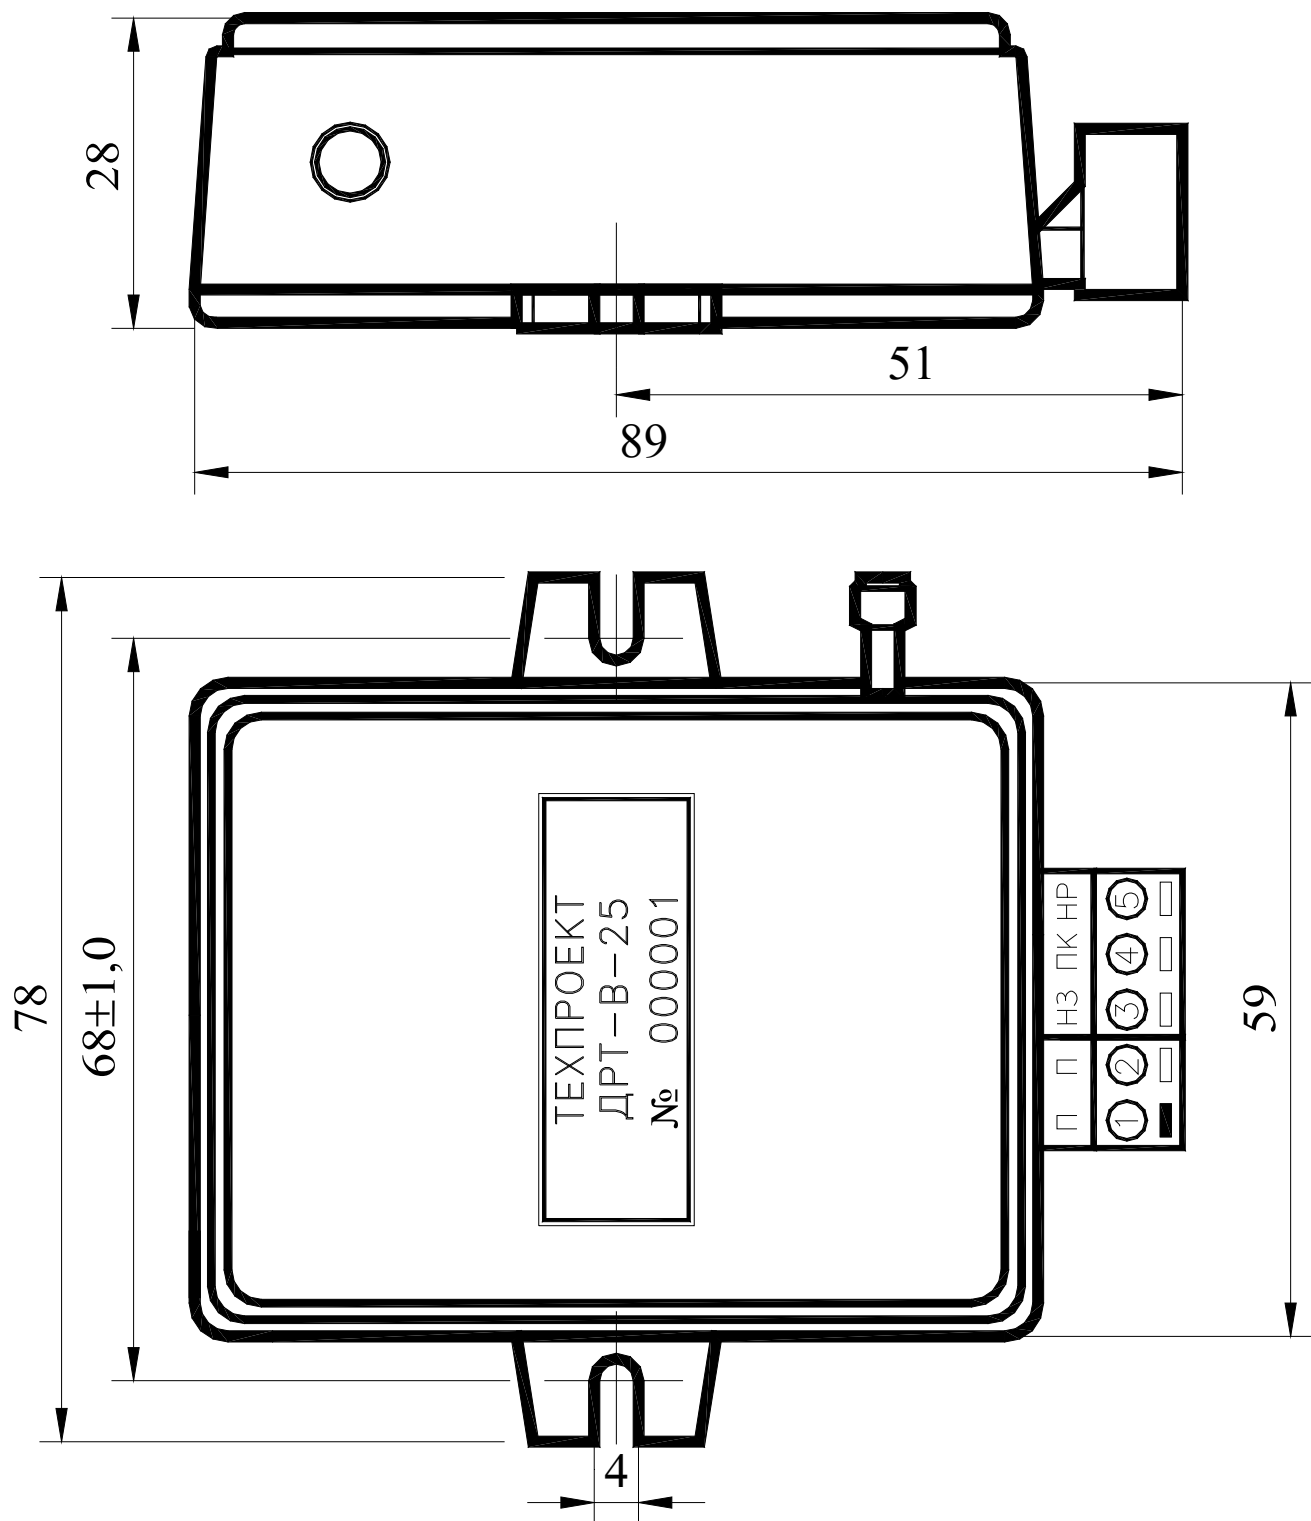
Габаритные размеры ДРТ-В ААРЛ.433647.006-02
